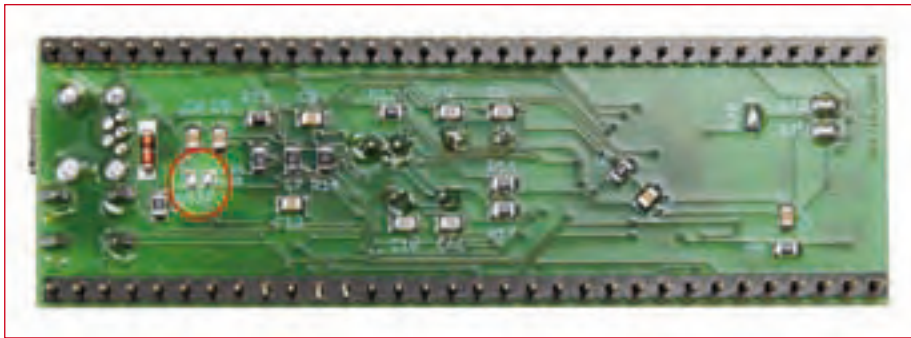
¡Antes de conectar la tarjeta del procesador con la Placa de Aplicación por primera vez, es imprescindible abrir los puentes de soldadura!
